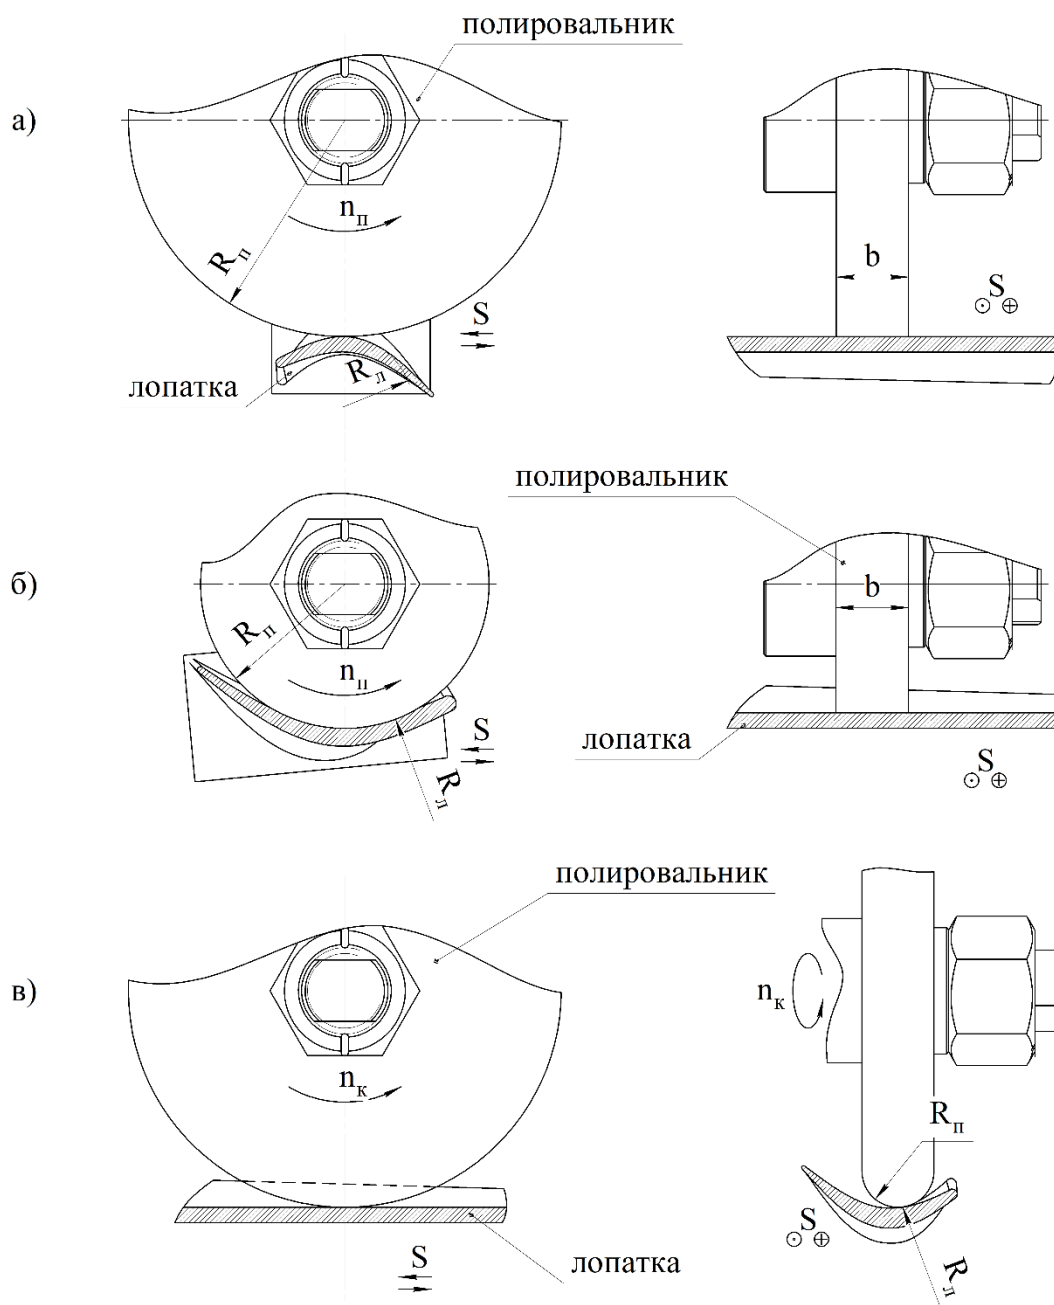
Основные схемы окончательной обработки элементов пера лопатки: а) обработка поверхности спинки лопатки; б) обработка корытца кругом, превышающим радиус обрабатываемой лопатки; в) обработка корытца кругом, радиус которого меньше обрабатываемого радиуса корытца
